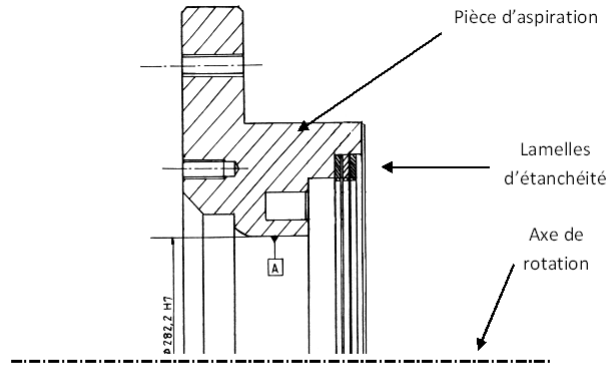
Utilisation de lamelles d'étanchéité
